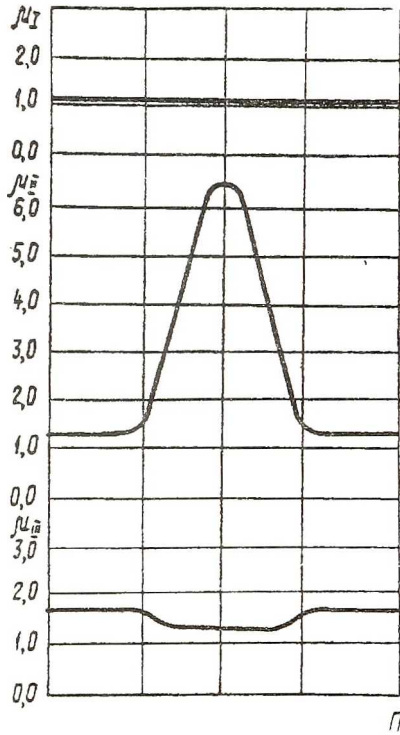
Вытяжки по переходам калибровки промежуточного кольца из сплава ВТ20 (рис. 4.20)
